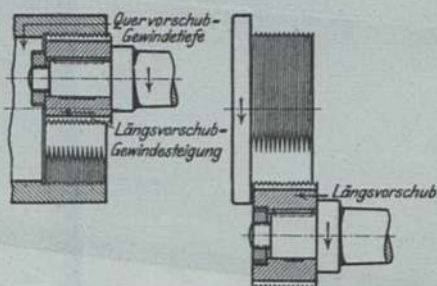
und 760. Gewindefräsen mit Rillenfräser.
